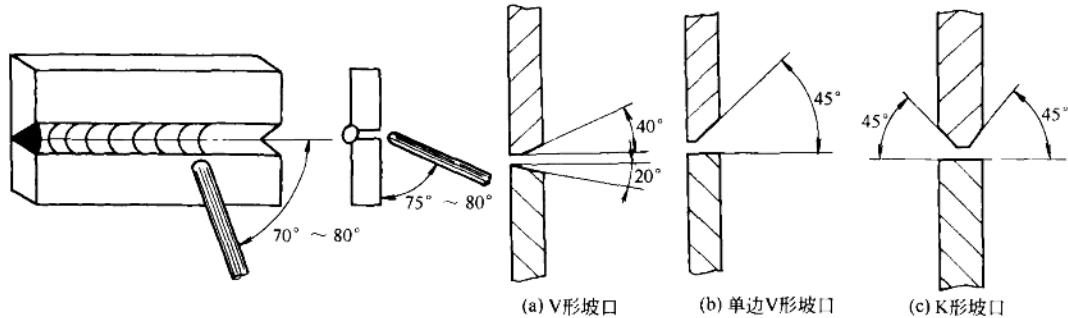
I形坡口的对接横焊时焊条角度
